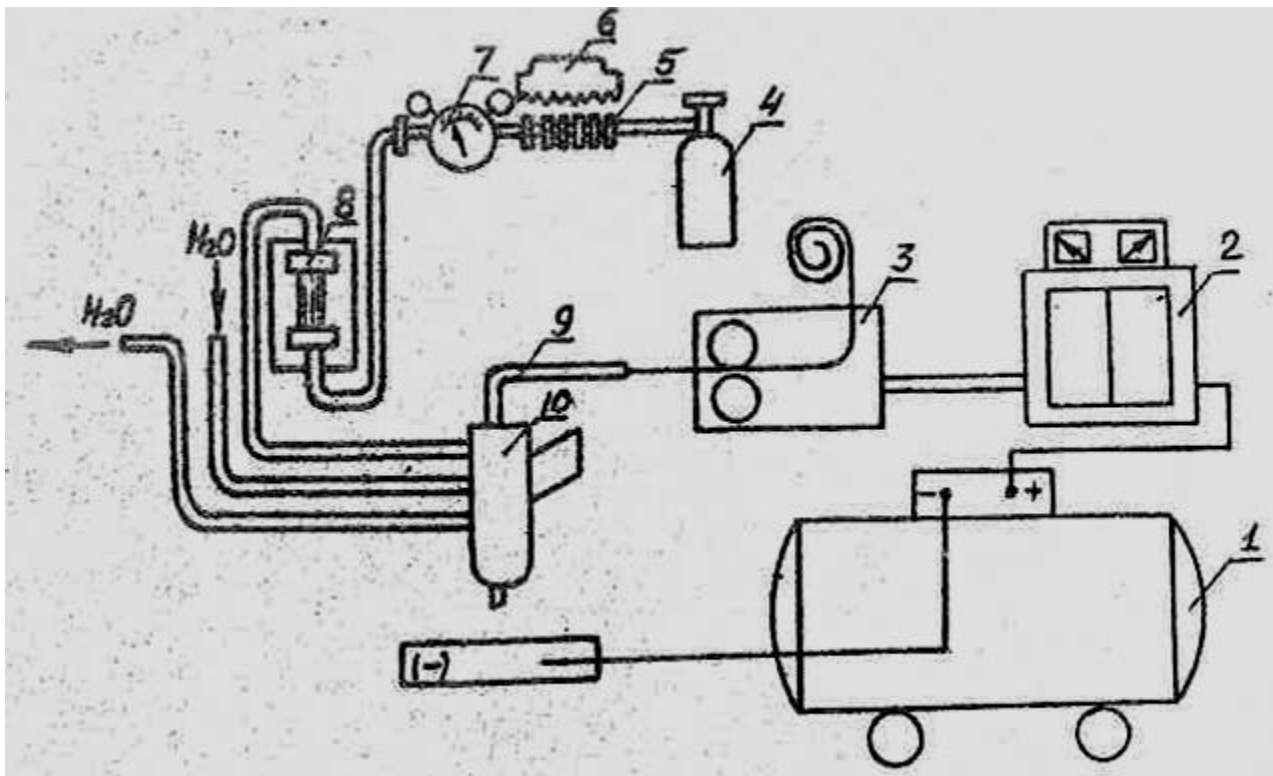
Схема установки для сварки в среде углекислого газа
